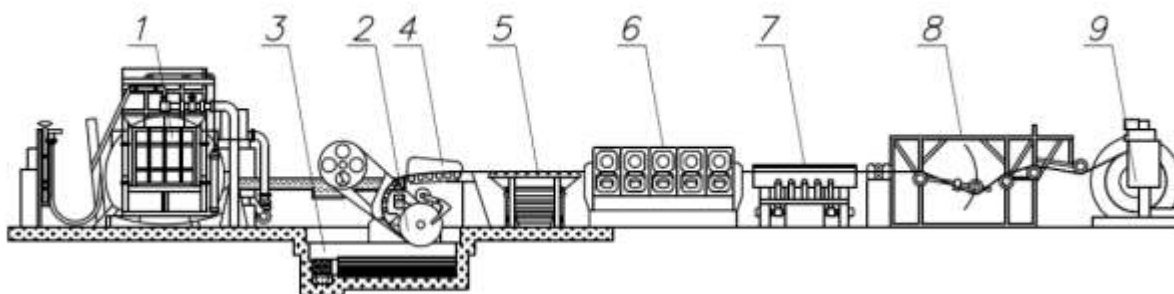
ЛПА CONTINUUS PROPERZI: 1- печь+миксер; 2-кристаллизатор; 3- литейная яма; 4- датчик автоматической разливки металла (АМР); 5- рольганг; 6- прокатный стан; 7- устройство для охлаждения и осветления; 8-натяжное устройство; 9- моталка
